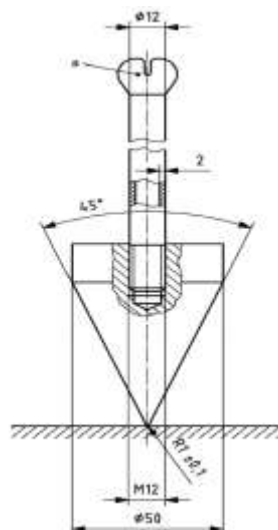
Схема конуса, свободно падающего на образец
